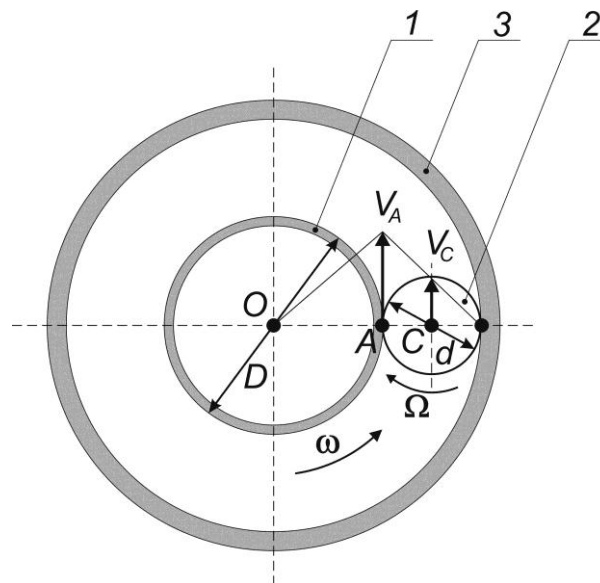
Схема радиального подшипника качения: 1 – внутреннее подвижное кольцо; 2 – тело качения; 3 – наружное неподвижное кольцо.
